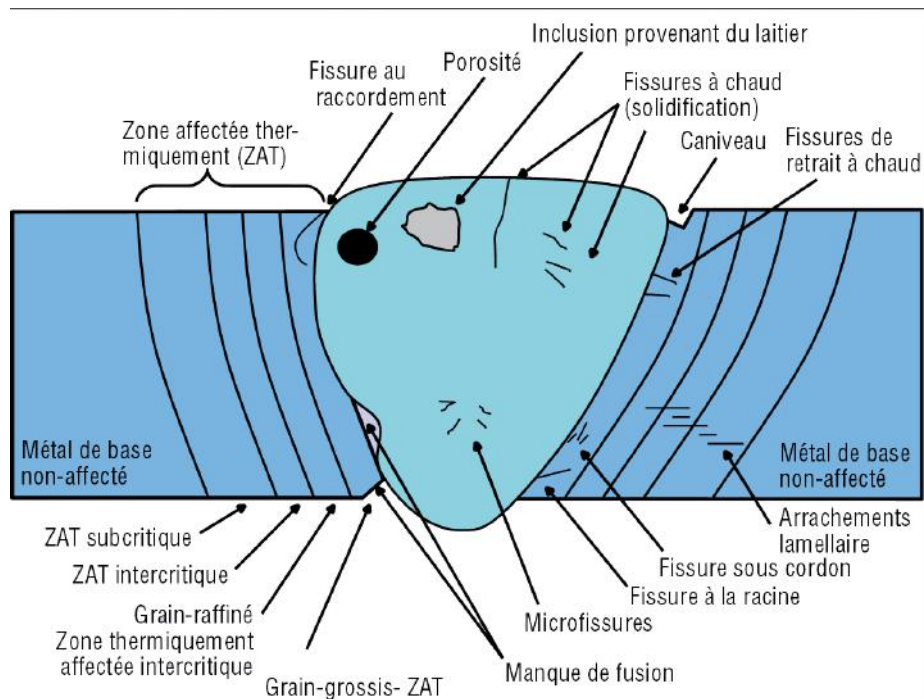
Schéma illustrant les différentes régions d'un joint de soudure suite à une soudure à passe unique et les défauts éventuels.
